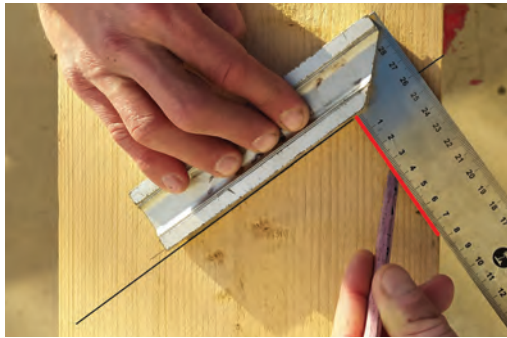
Línea roja: perpendicular de H. Fuente: autor.
